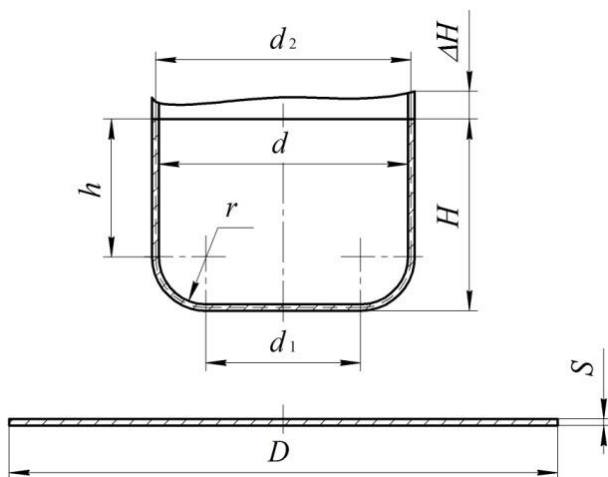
Расчетная схема при вытяжке без утонения стенки
